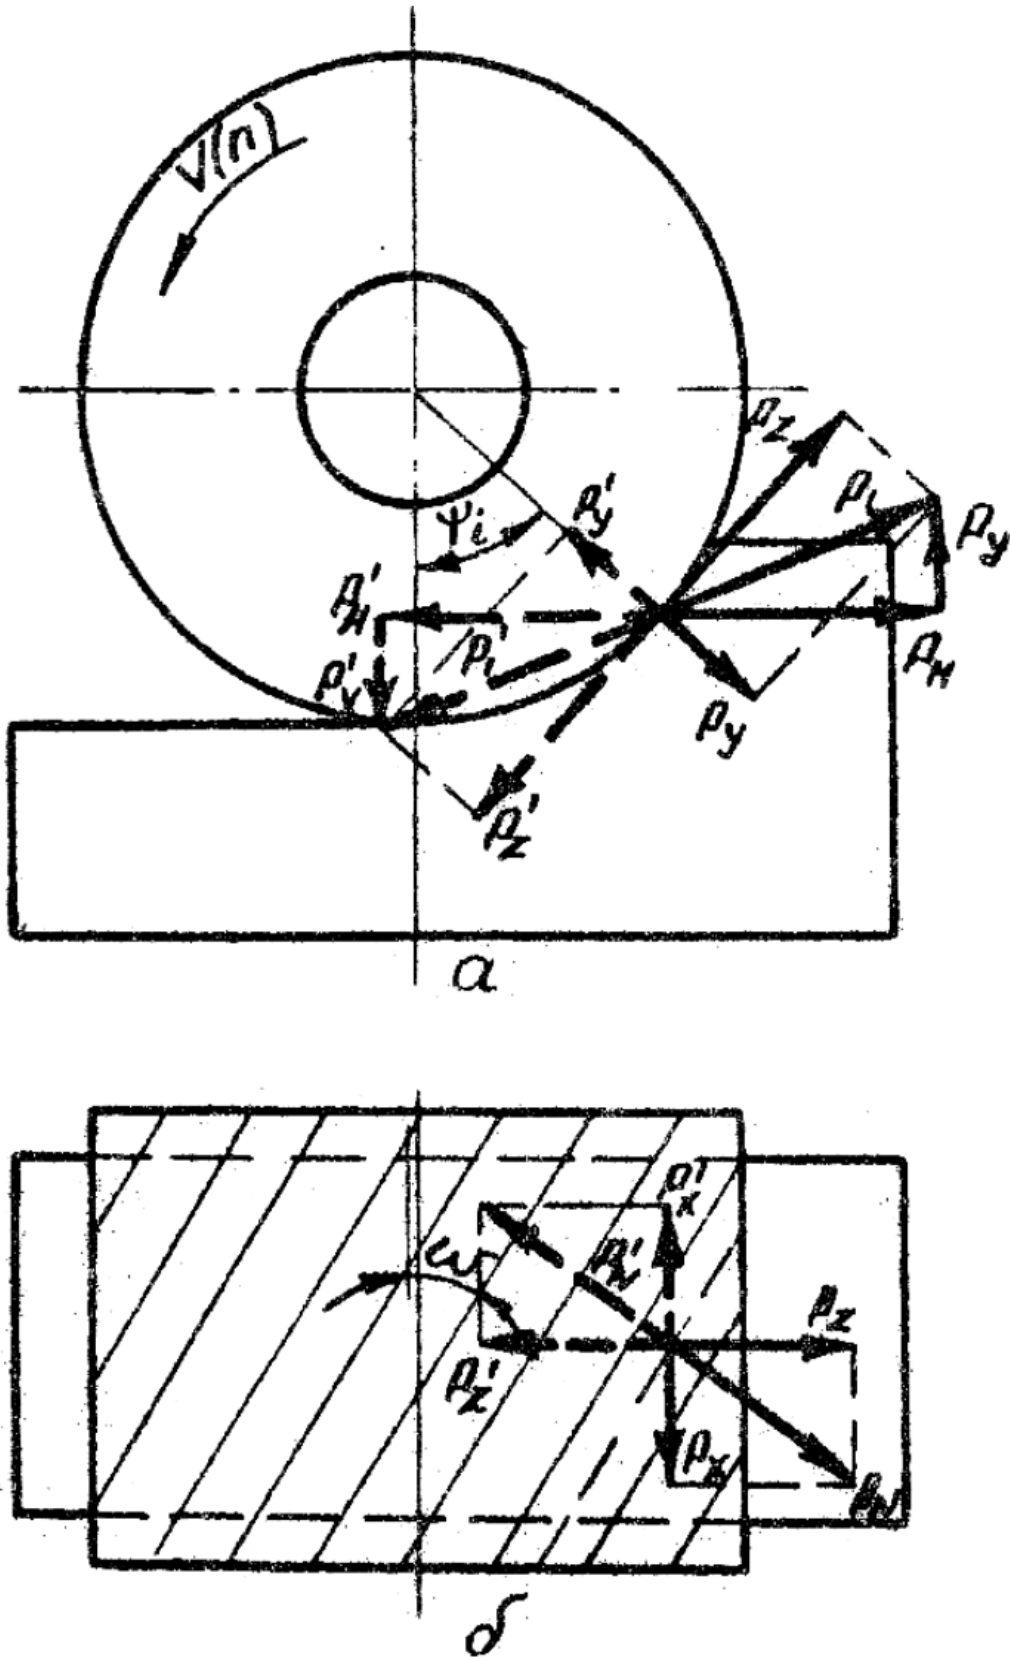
Сили різання при циліндричному фрезеруванні фрезою з гвинтовим зубом: а – сили P_z , P_y , P_x , що діють на заготовку; б – сили P'_z , P'_y , P'_x , що діють на фрезу.
